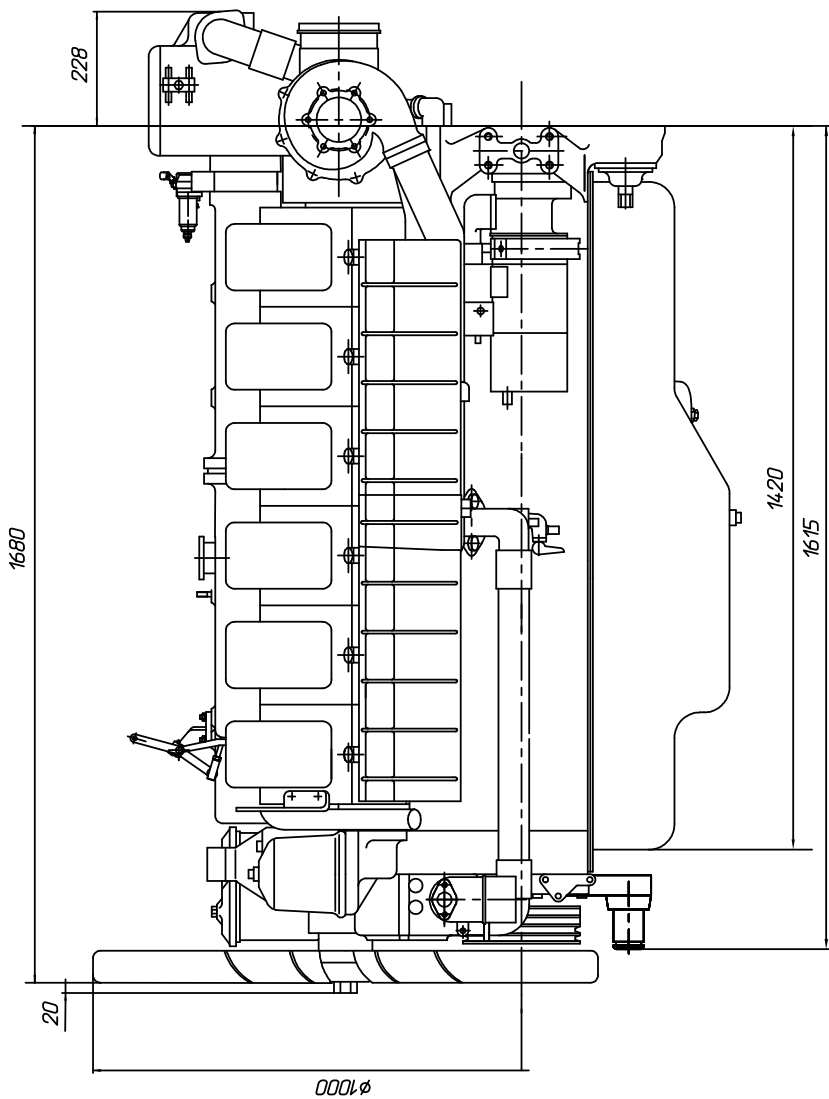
Габаритные размеры двигателя (вид слева)
